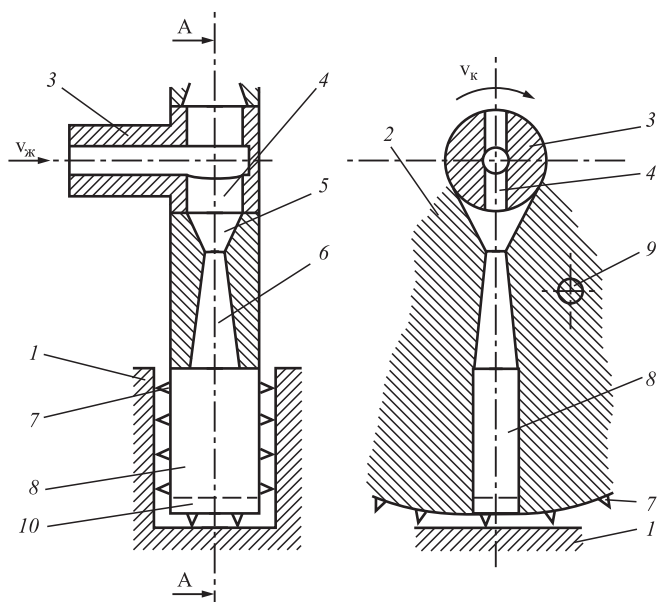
Регулируемый подвод жидкой рабочей среды через корпус инструмента:
